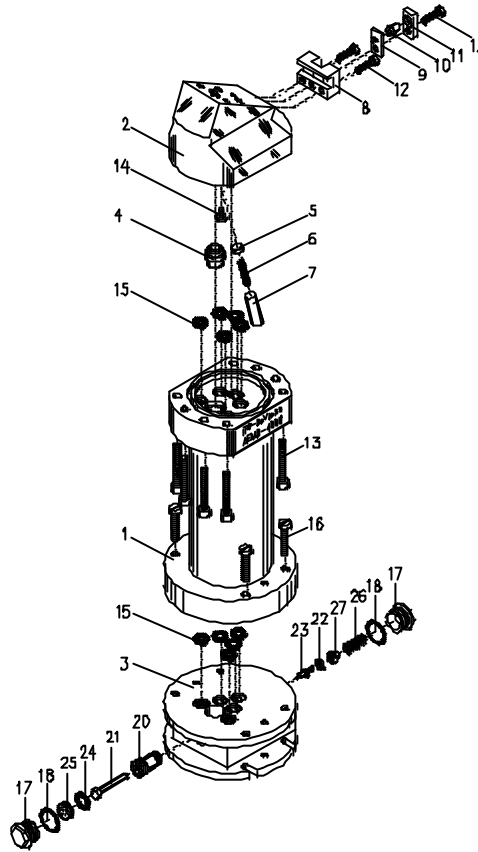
Adaptateur AEMD 4500 pour machine
